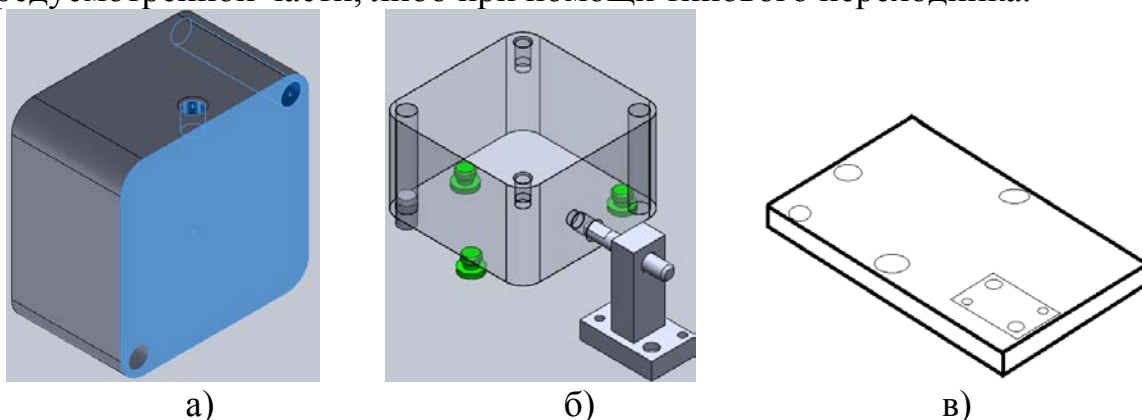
Исходная модель детали (а), компоновка приспособления (б), корпусная плита
